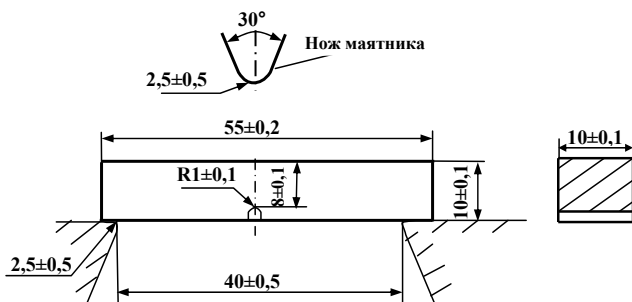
Форма и размеры образца для испытаний на ударную вязкость
